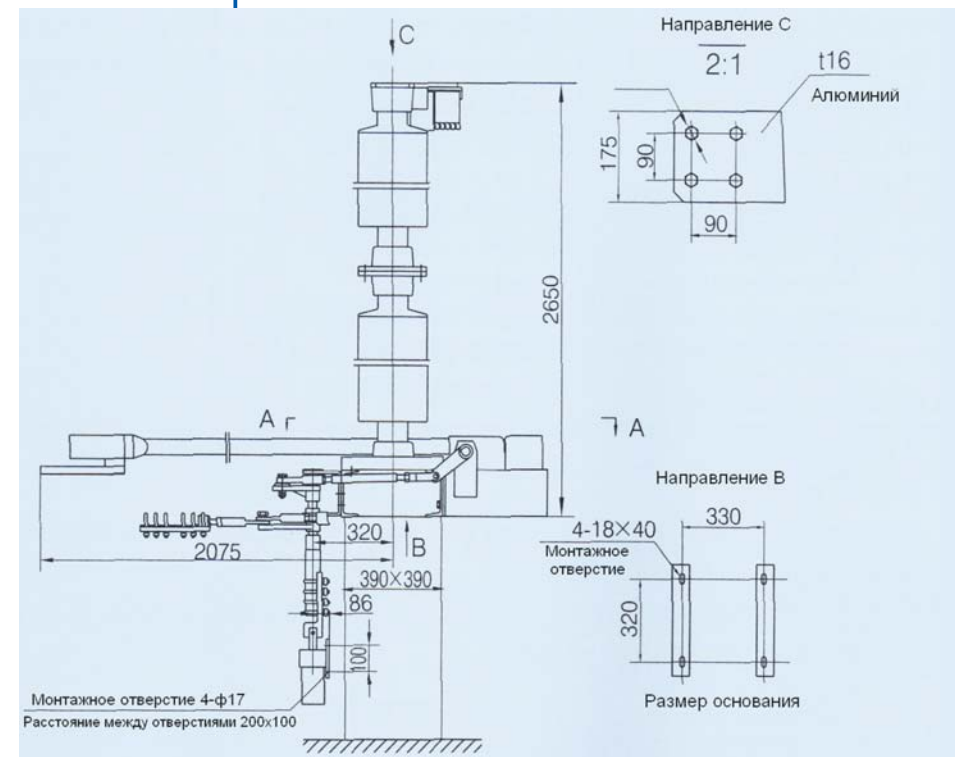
Внешний вид и размеры заземлителя JW□-252
